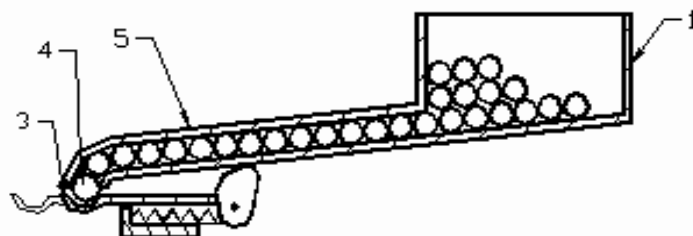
Схема автоматического загрузочного устройства для штучных заготовок деталей
